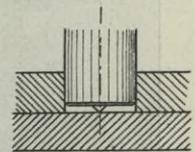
Bezeichnung des Stabendes mit Feinkörnerschlägen.
